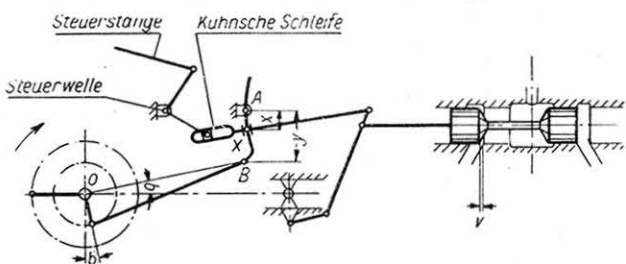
Gesamtbild der Heusinger-Steuerung für innere Einstromung
